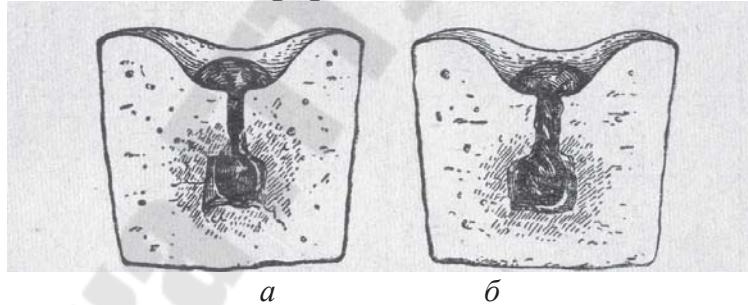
Дефекты отливки: *а* – недолив из-за преждевременного затвердения металла: *б* – завихрение жидкого металла и усадочные раковины
